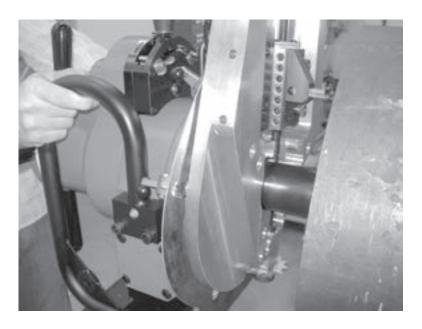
Poussez la machine vers l'avant sur le mandrin jusqu'à ce que vous puissiez engager les filets du mandrin sur l'écrou d'avance.
